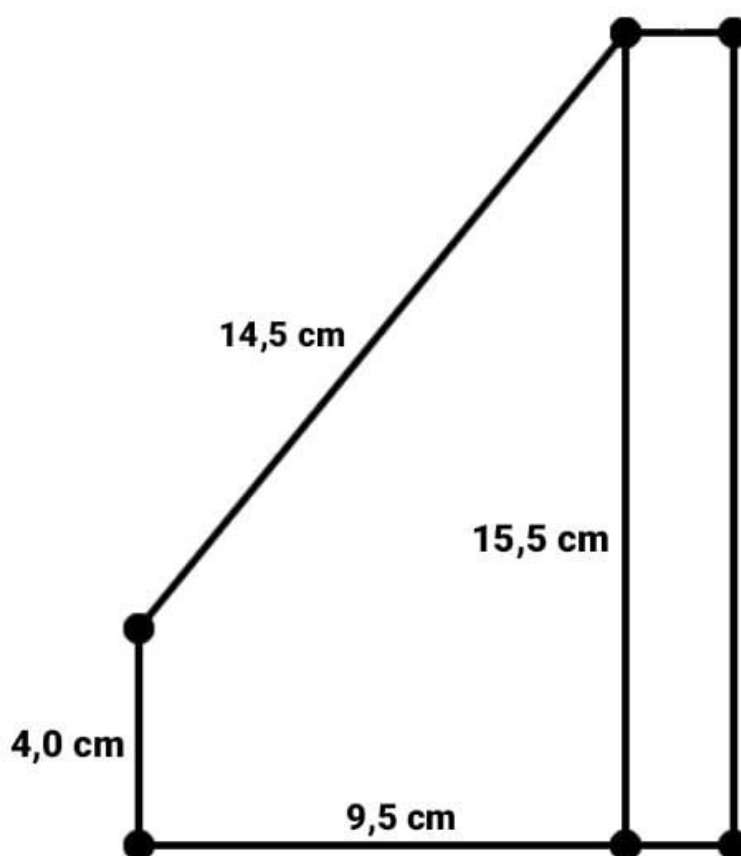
Molde das aletas do foguete. Fonte: autores.
